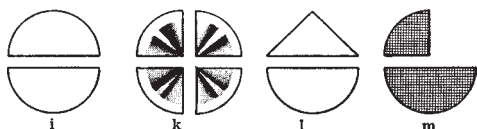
Untere Seite von vier Fassungswerkzeugen;
